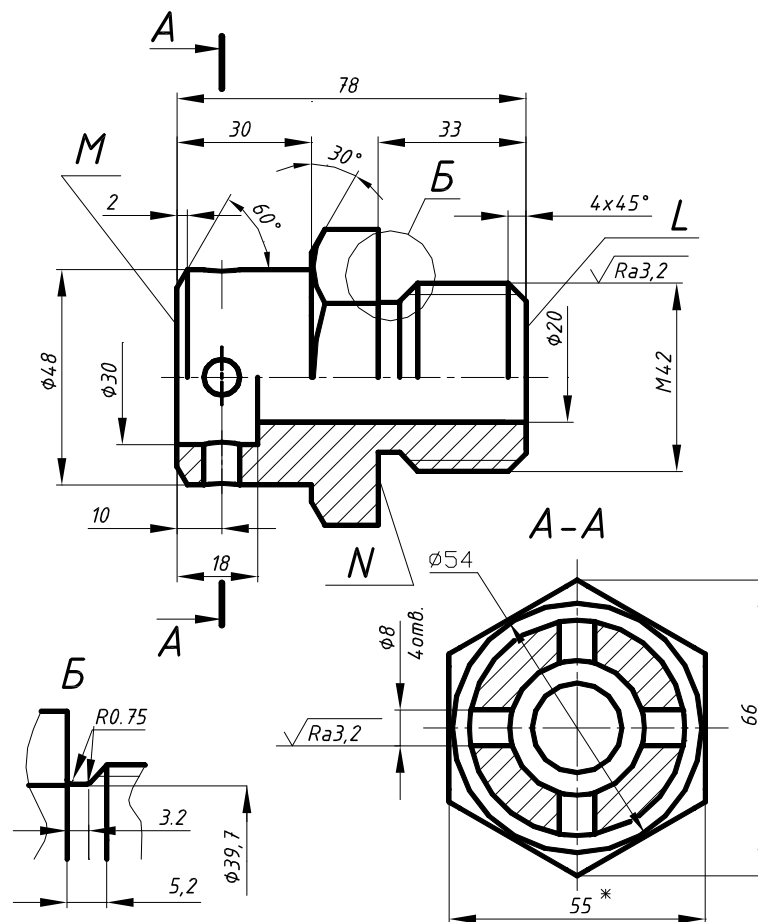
Деталь, изготовленная различной механической обработкой
